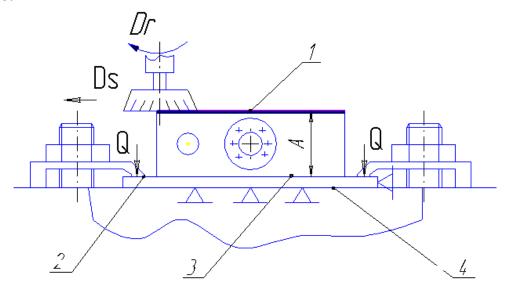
Схема обработки заготовки, установленной в приспособление
